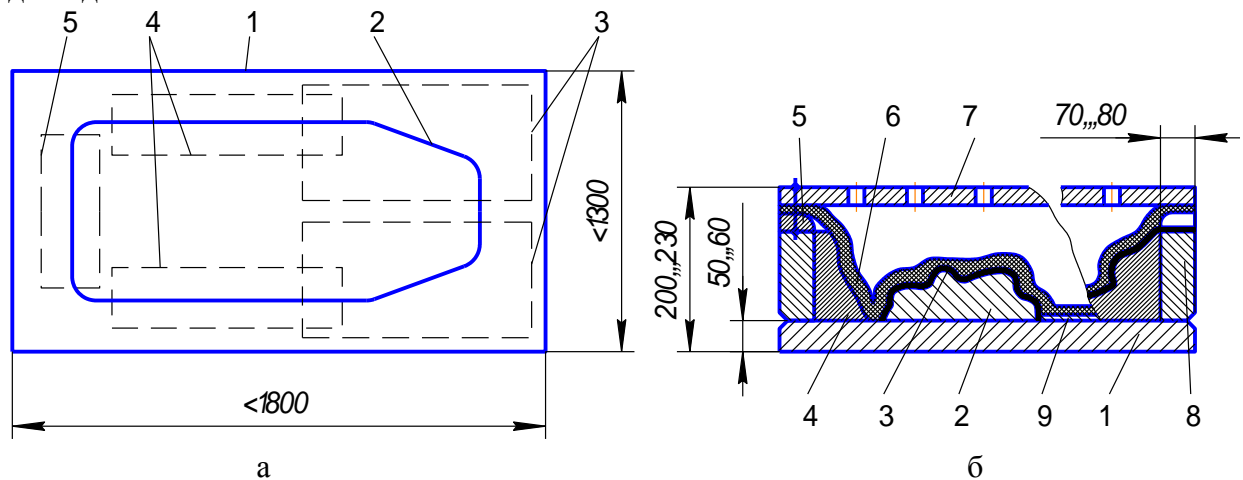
Варіанти схем універсального оснащення для витяжки й формування: а – варіант розташування формозадаючих поверхонь на робочій поверхні універсальної матриці для штампування деталей на пресі ПЕГ-ХАІ-500: 1 – зовнішній контур матриці; 2 – універсальний контур перерізу матриці; 3 – зони розташування заготовок для штампування кутових панелей передньої частини даху; 4 – зони розташування заготовок для штампування бокових панелей даху; 5 – зона розташування заготовок для штампування середньої частини передньої панелі даху; б – варіант універсального контейнера для розміщення формблоків для штампування деталей на пресі ПЕГ-ХАІ-500: 1 - зварений контейнер; 2 - оправка для формування листової заготовки; 3 - відштампована деталь; 4 - кутова вставка; 5 - притискна плита; 6 - гумова діафрагма; 7 - напрямна плита багатоелектродного розрядного блок; 8 - варіант витяжної матриці в контейнері; 9 - гумовий коврик
